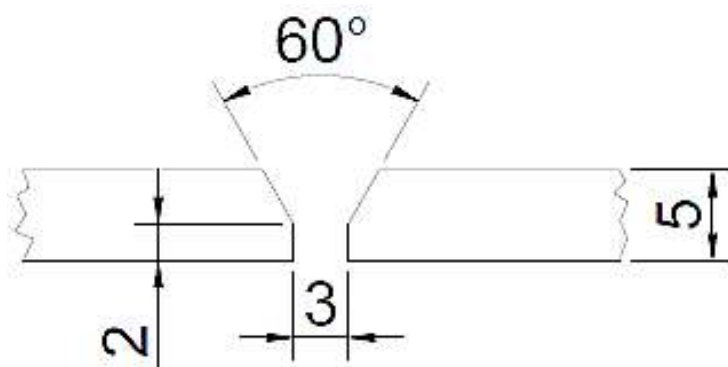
Dimensiones de la junta de soldadura⁹⁰
